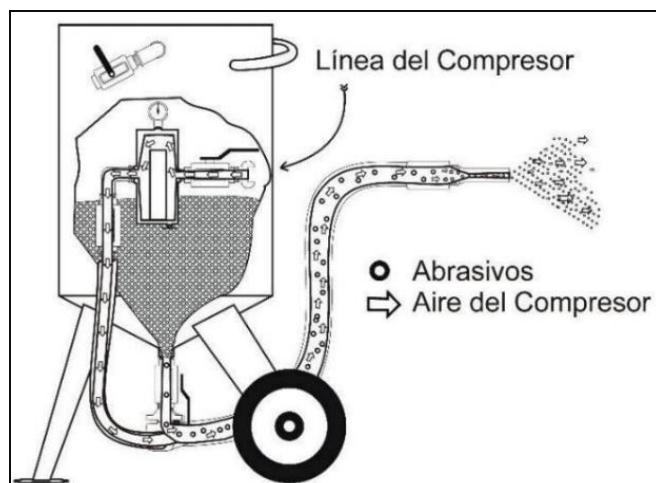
Sistema de sandblasting [Fuente: www.chipaxa.com]
